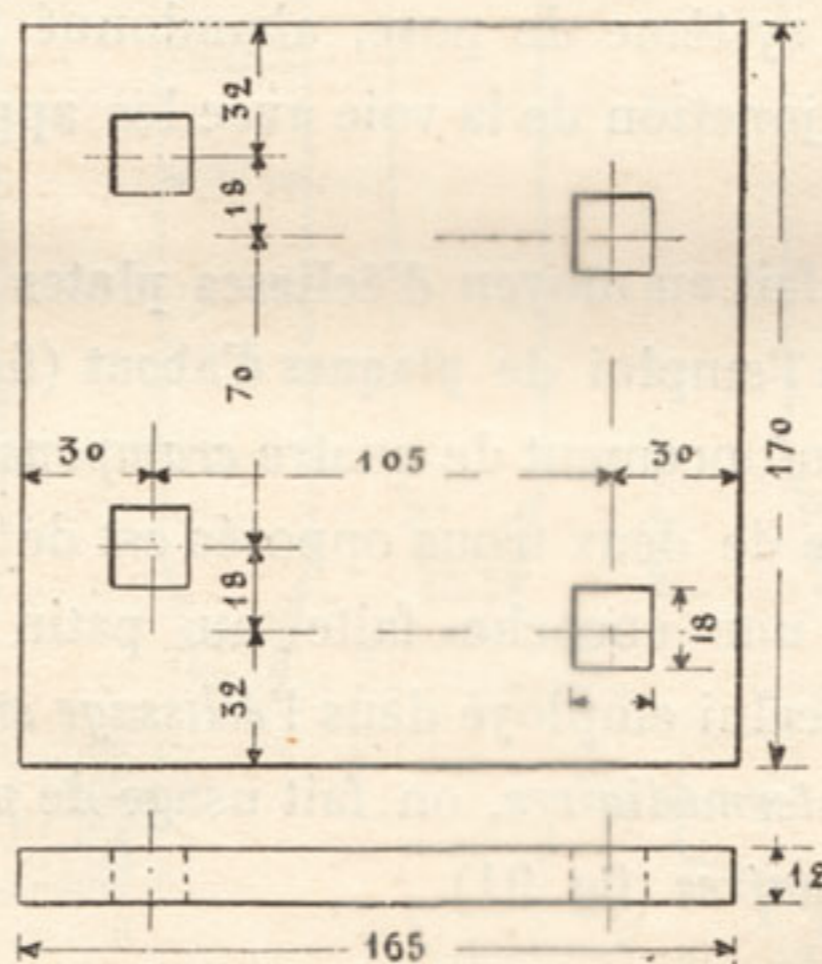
Plaque d'about pour rail de 38 kgr. Echelle 1/4.
